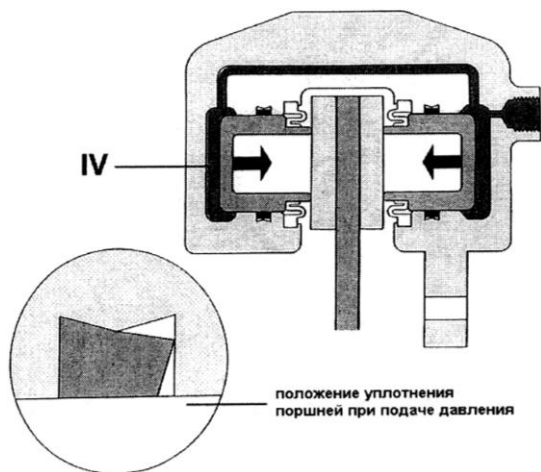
Схема положения деталей дискового тормозного механизма с неподвижным суппортом при торможении
